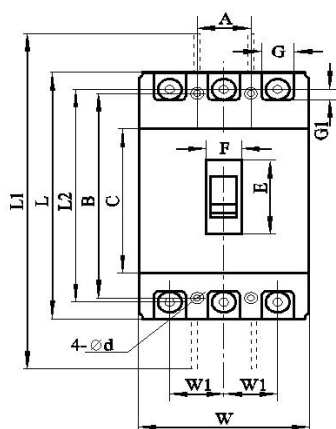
Габаритные и установочные размеры выключателей BA77-63, BA77-125, BA77-250.
